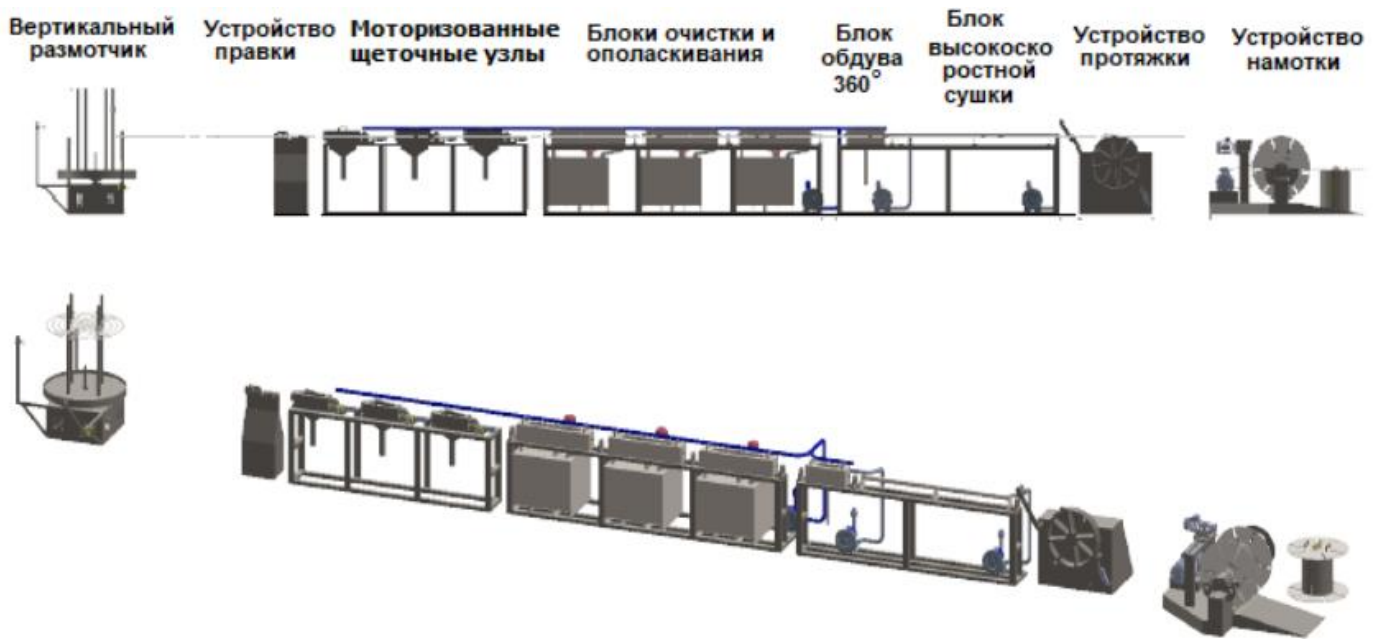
Схема размещения элементов линии очистки и намотки сварочной проволоки.
